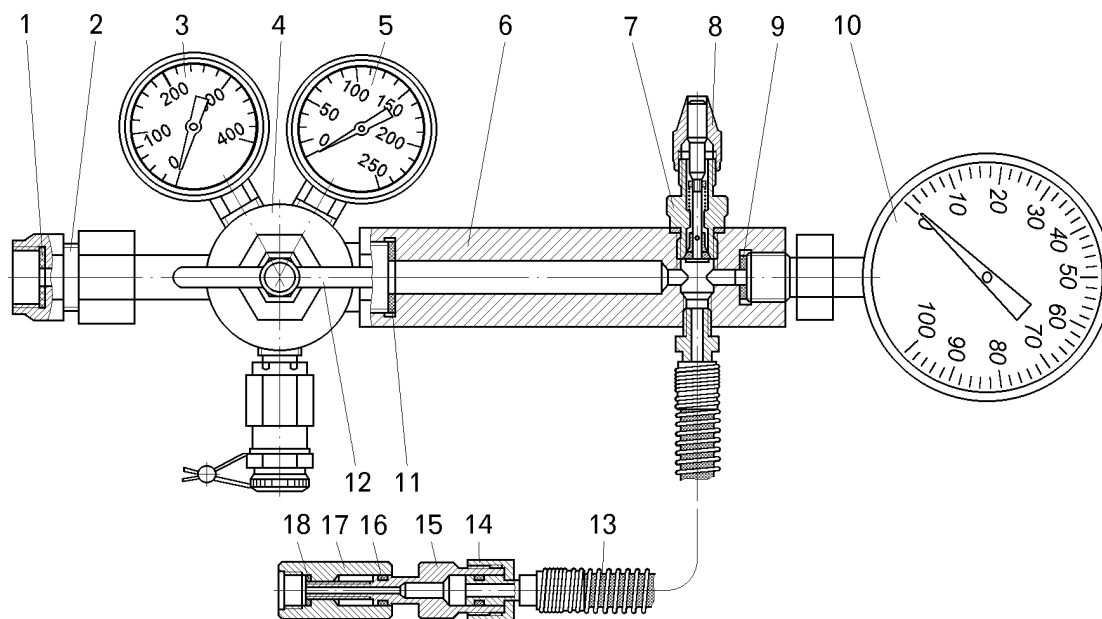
Приспособление для зарядки цилиндров подвески:
